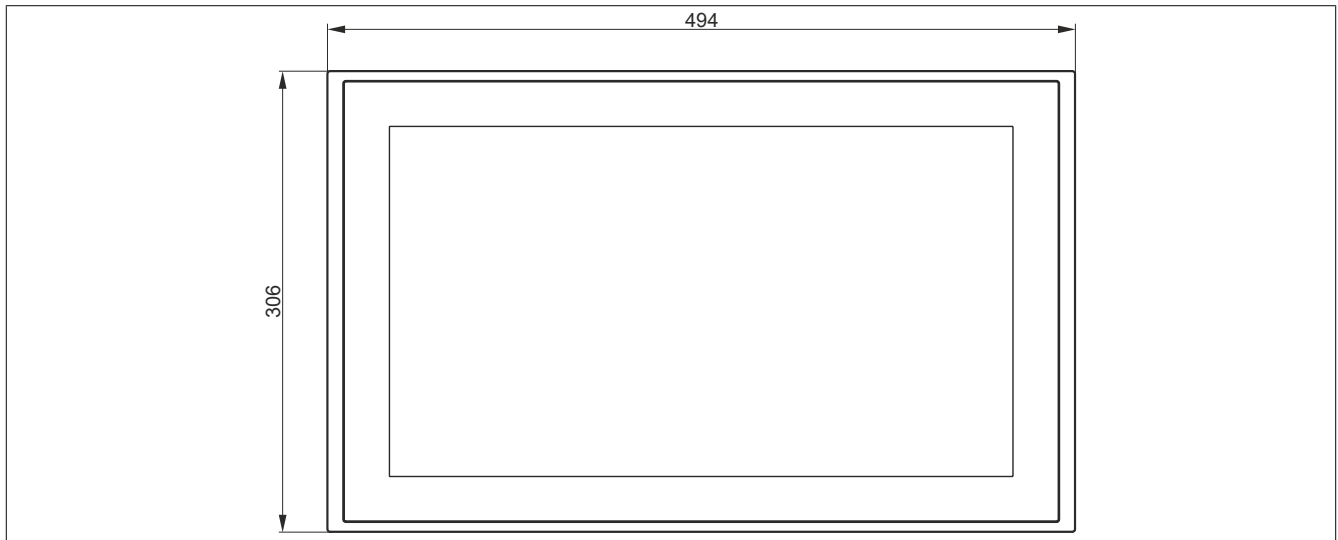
5AP5130.185C-000 - Abmessungen
